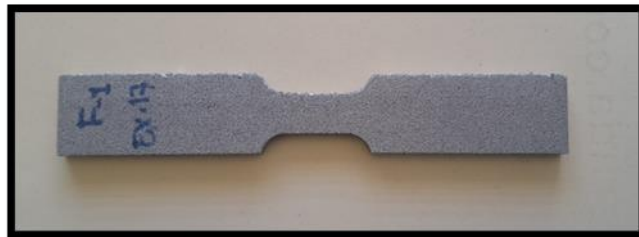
Material de Prueba para ensayo de fatiga fabricado por SLM.
